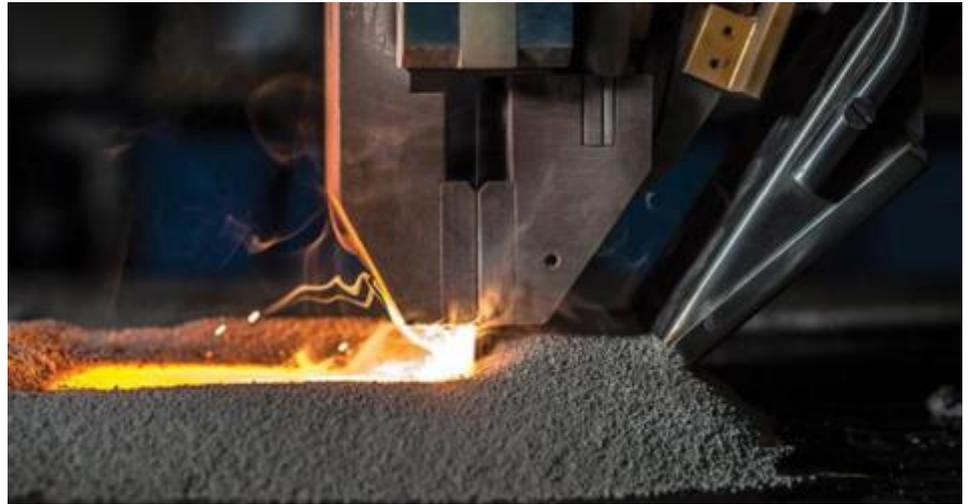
Soldadura bajo electroescoria.[3]
